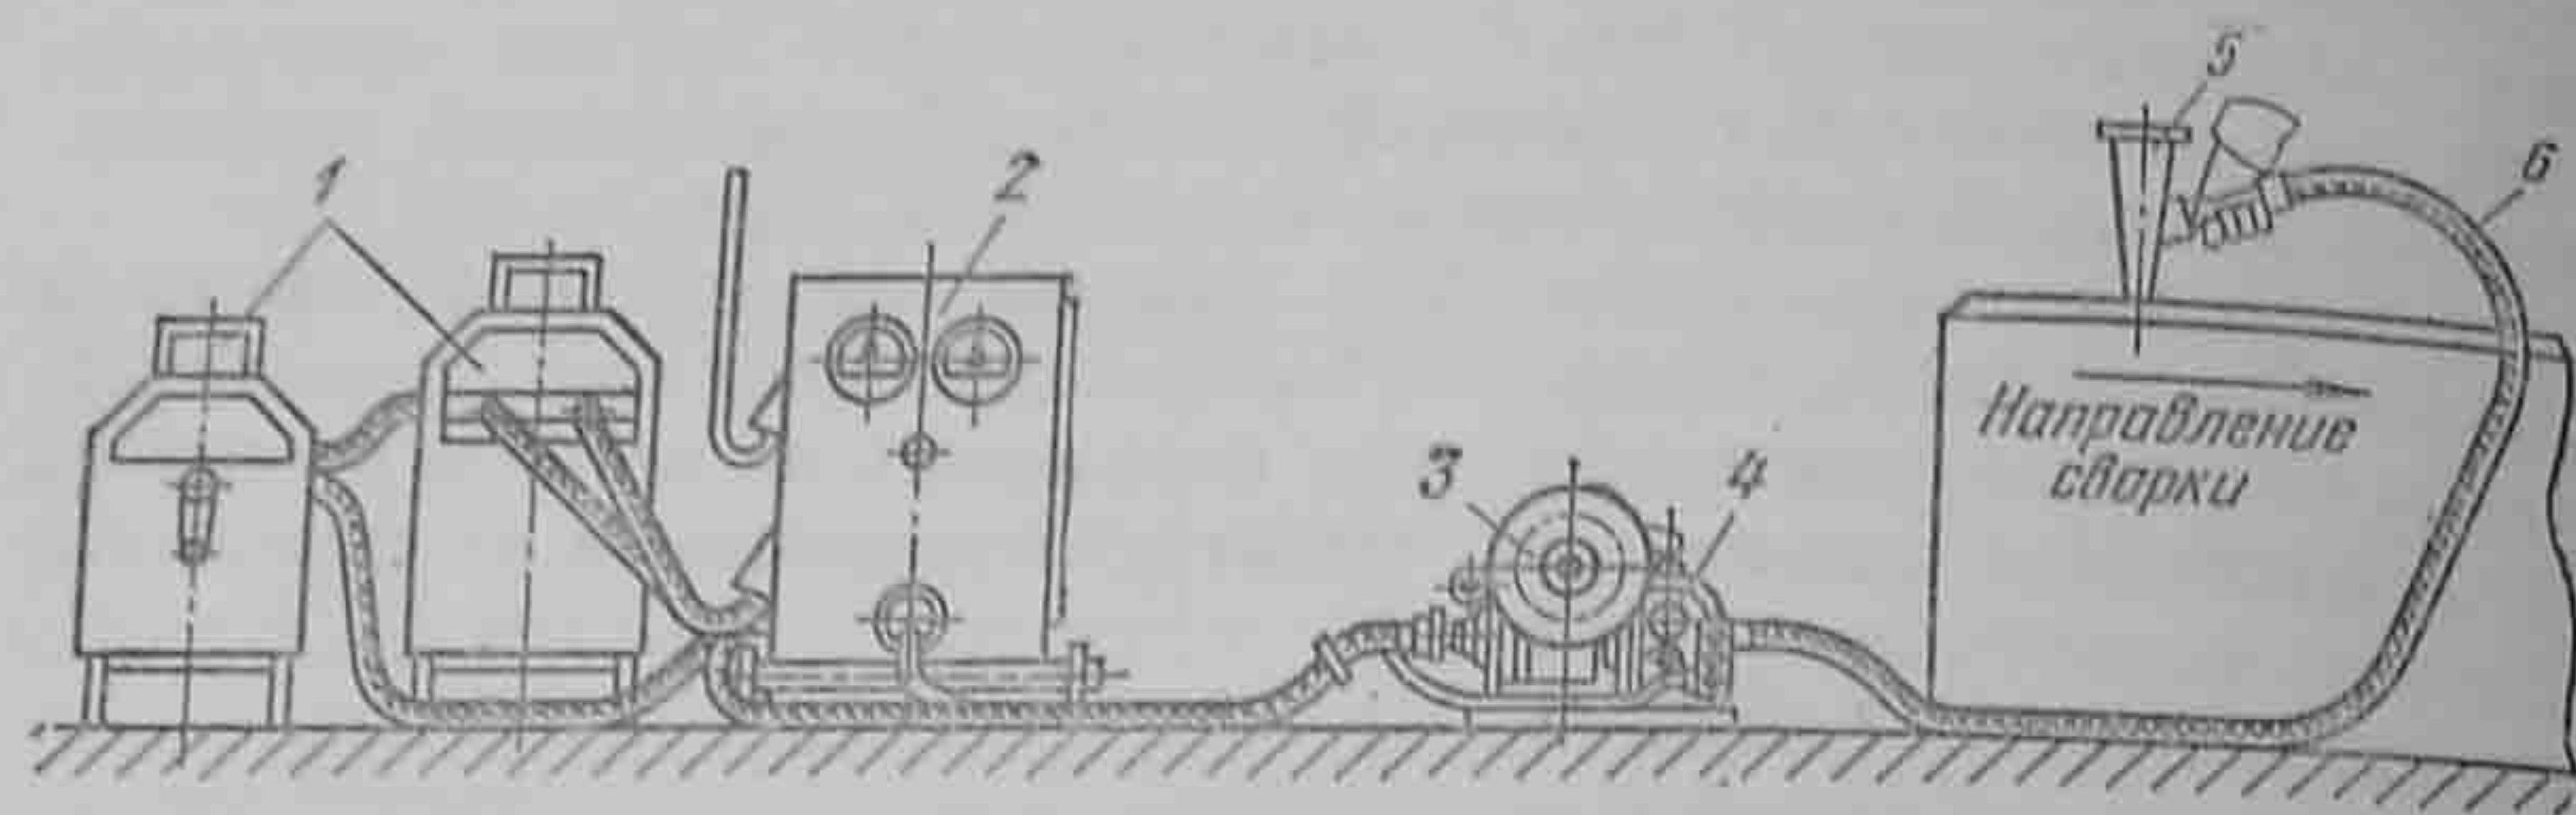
Шланговый полуавтомат для сварки под флюсом
